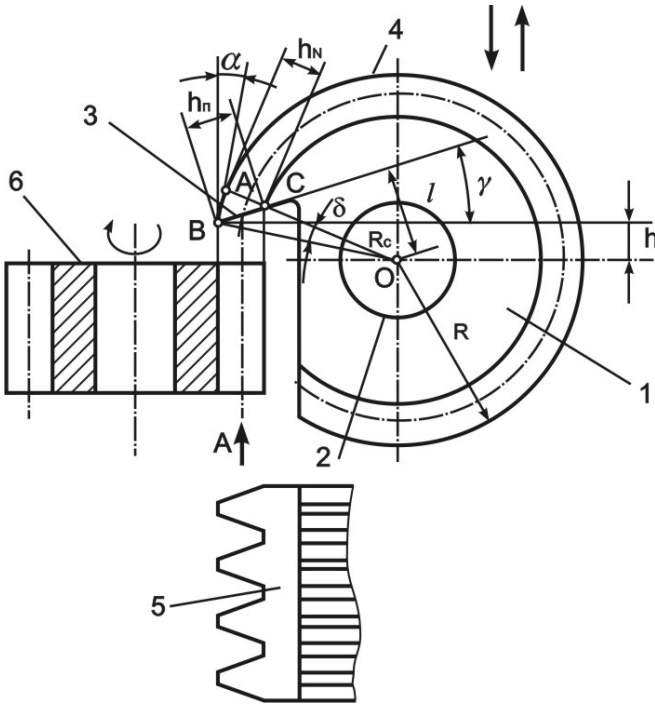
Схема обробки гребінкою, затилюваною по колу
